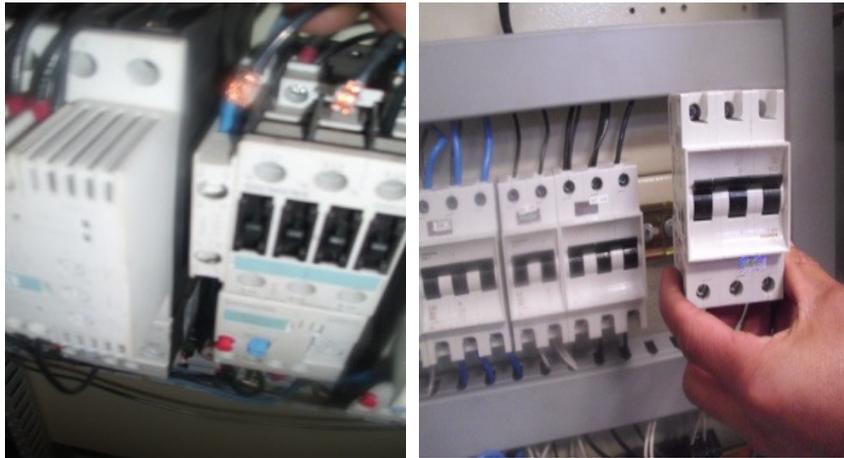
Instalación del sistema de fuerza máquina de secado
